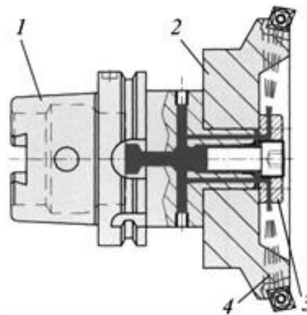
Подача СОТС к режущим пластинам торцевой фрезы:
